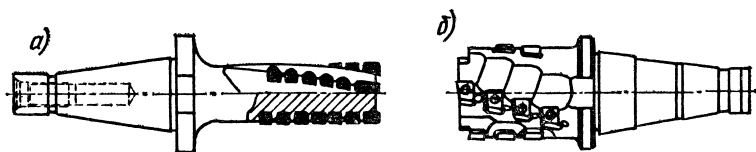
Фрезы твердосплавные для обдирочных работ
